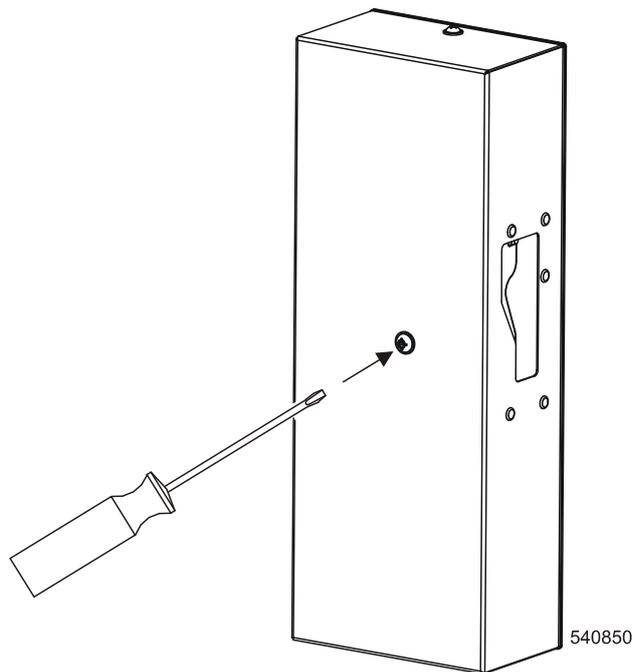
B Máquinas 80-100-120 kg / 180-230-275 lbs, cerradura
